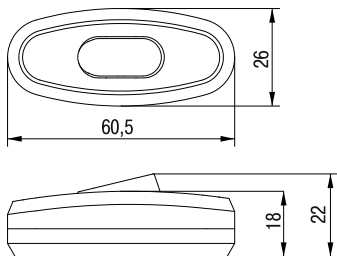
Габаритные размеры выключателей ВБ-01Б и ВБ-01Ч
